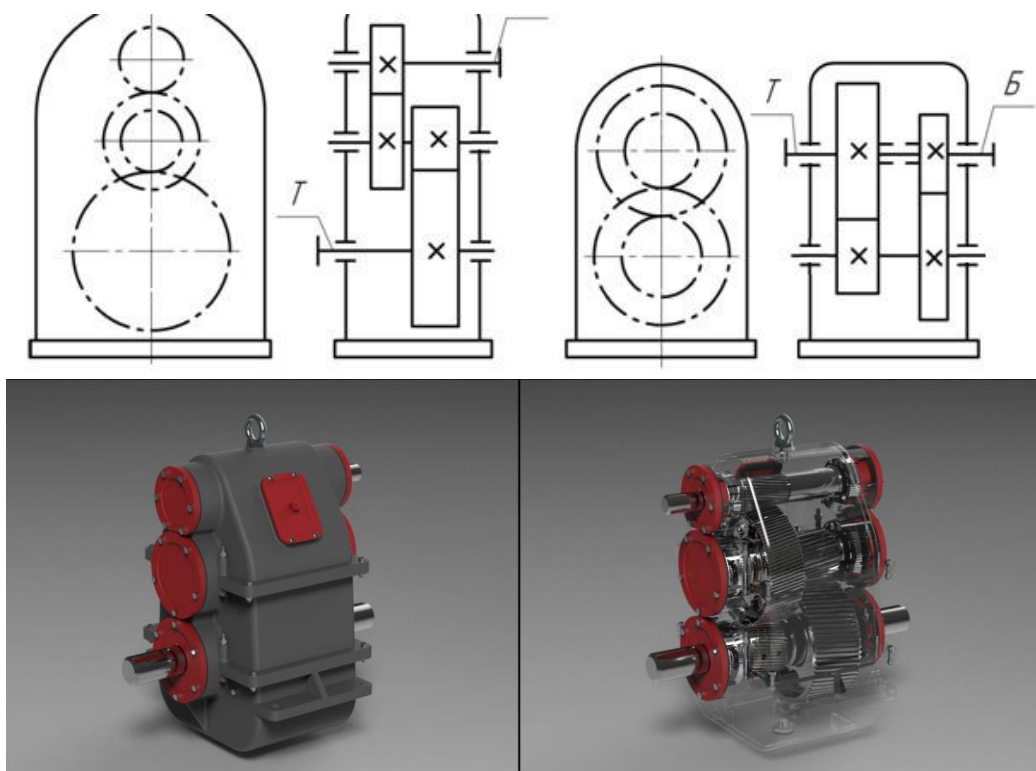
Двухступенчатые цилиндрические вертикальные редукторы
